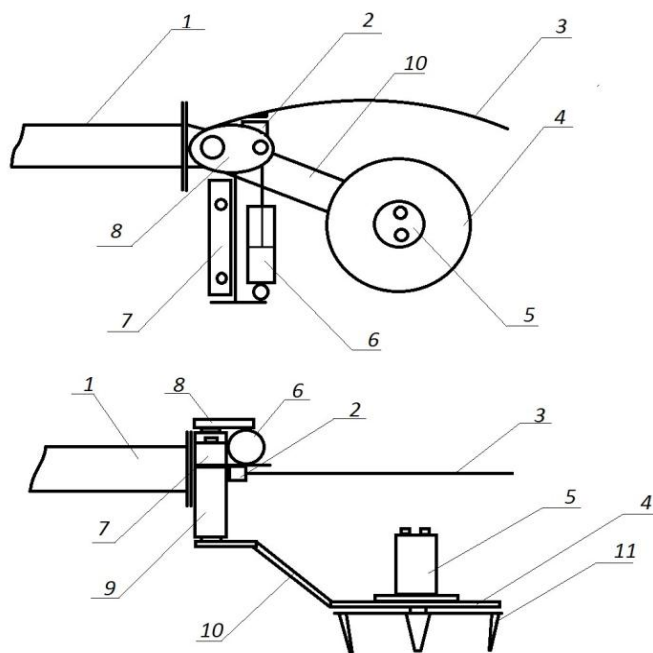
Конструктивно – технологическая схема предлагаемой фрезы с вертикально – роторным валом вращения для обработки приствольной зоны плодовых деревьев
